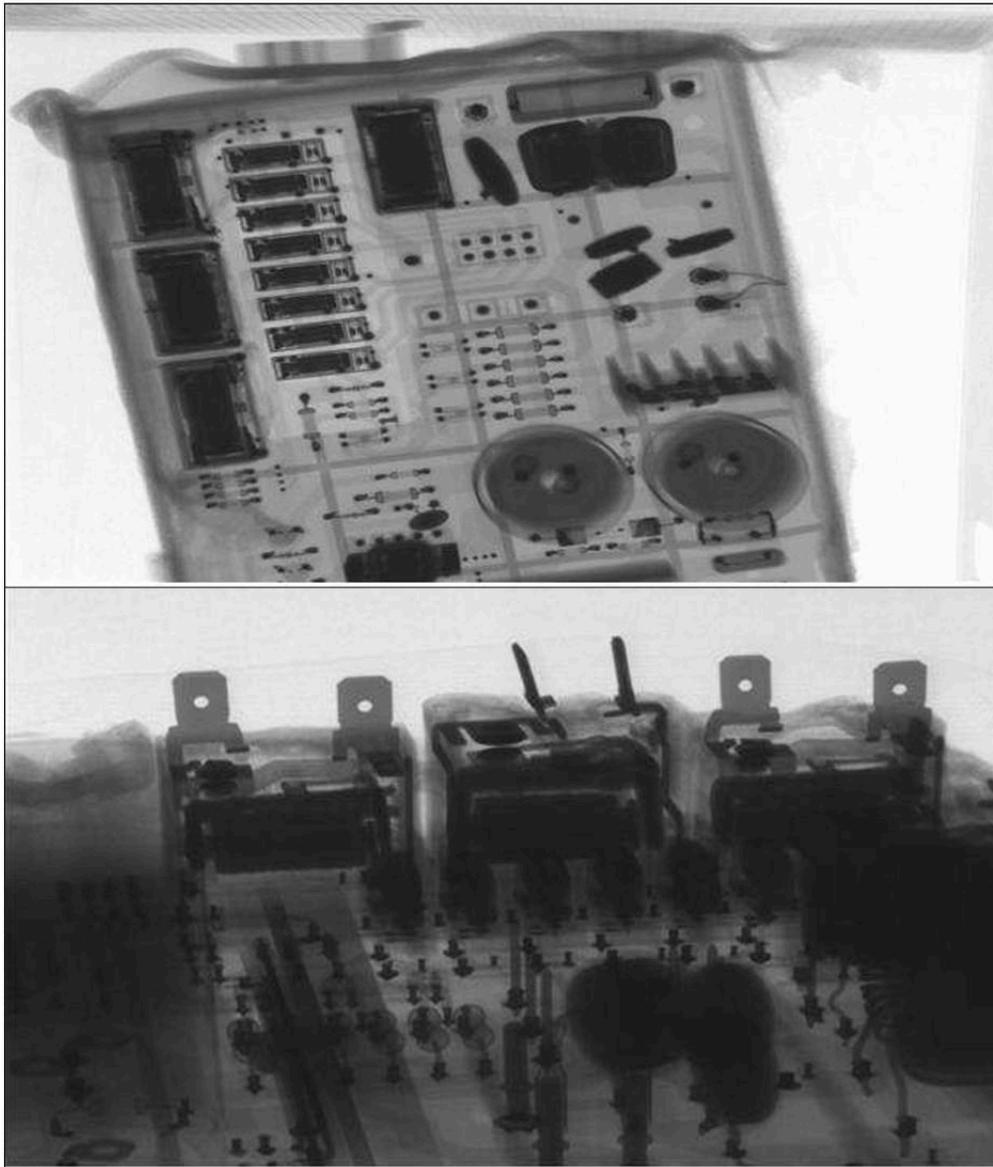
드럼세탁기 PCB(비파괴 사진)
